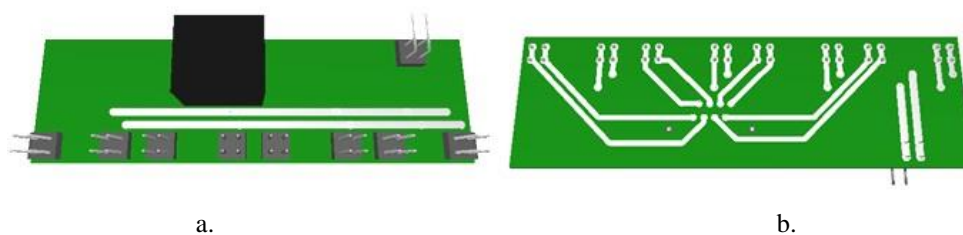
Layout* em 3D do protótipo da placa auxiliar de conexão dos drivers: a. face superior; b. face inferior
